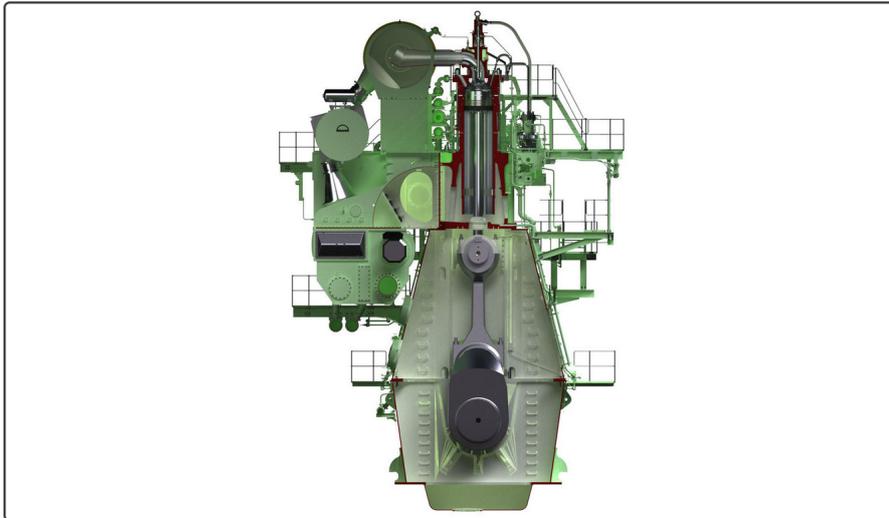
MAN-Großdieselmotor S90ME-C10.2. Zweitakt-Kreuzkopfmotor mit 900 mm-Bohrung und 6.100 kW pro Zylinder.
